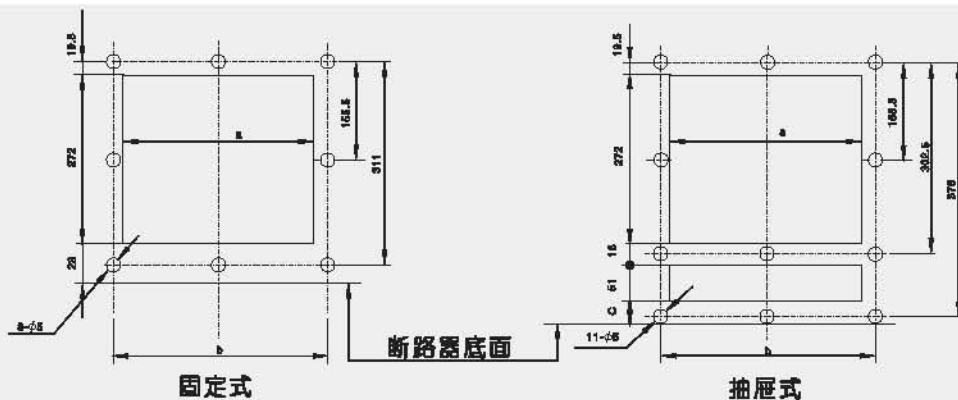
抽屉式断路器安装尺寸及外形尺寸 (HZW66-6300 In=6300A)
